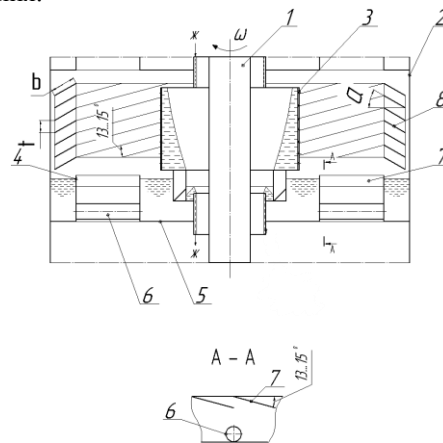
Схема исследуемой конструкции КЭ: 1 – вал; 2 – корпус; 3 – диспергирующее устройство; 4 – газоходы; 5 – сливная тарелка; 6 – переточные трубы; 7 – направляющие лопатки; 8 – пристенный каплеотбойник
